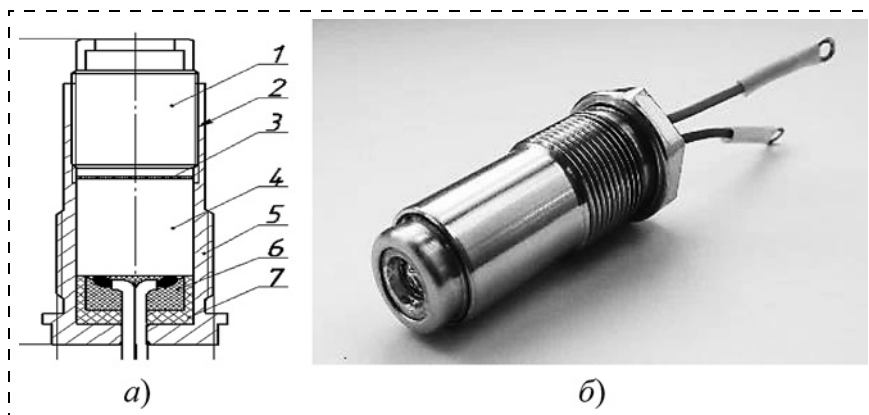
Конструктивная схема устройства с задействованием от корпуса (накаленной поверхности) (а), где 1 — замедлитель; 2 — герметик УГ-6; 3 — заряд из воспламенительной ЭКС; 4 — источник тока; 5 — корпус устройства; 6 — компаунд К-153к; 7 — упор; внешний вид устройства (б)
